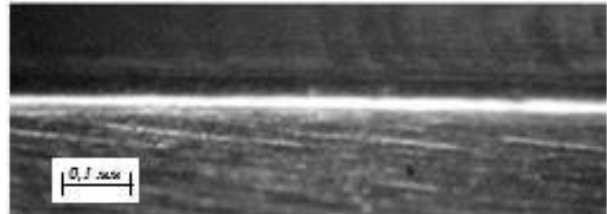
Зовнішній вигляд РК шпонкових фрез після МАО
